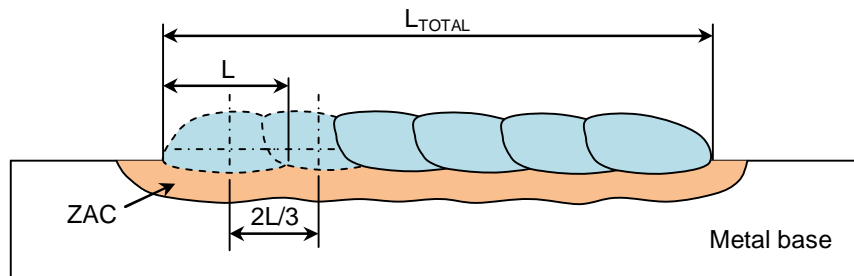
Desenho esquemático de sobreposição dos cordões de solda indicando o passo de sobreposição de $2/3L$, onde L é a largura do cordão inicial.
